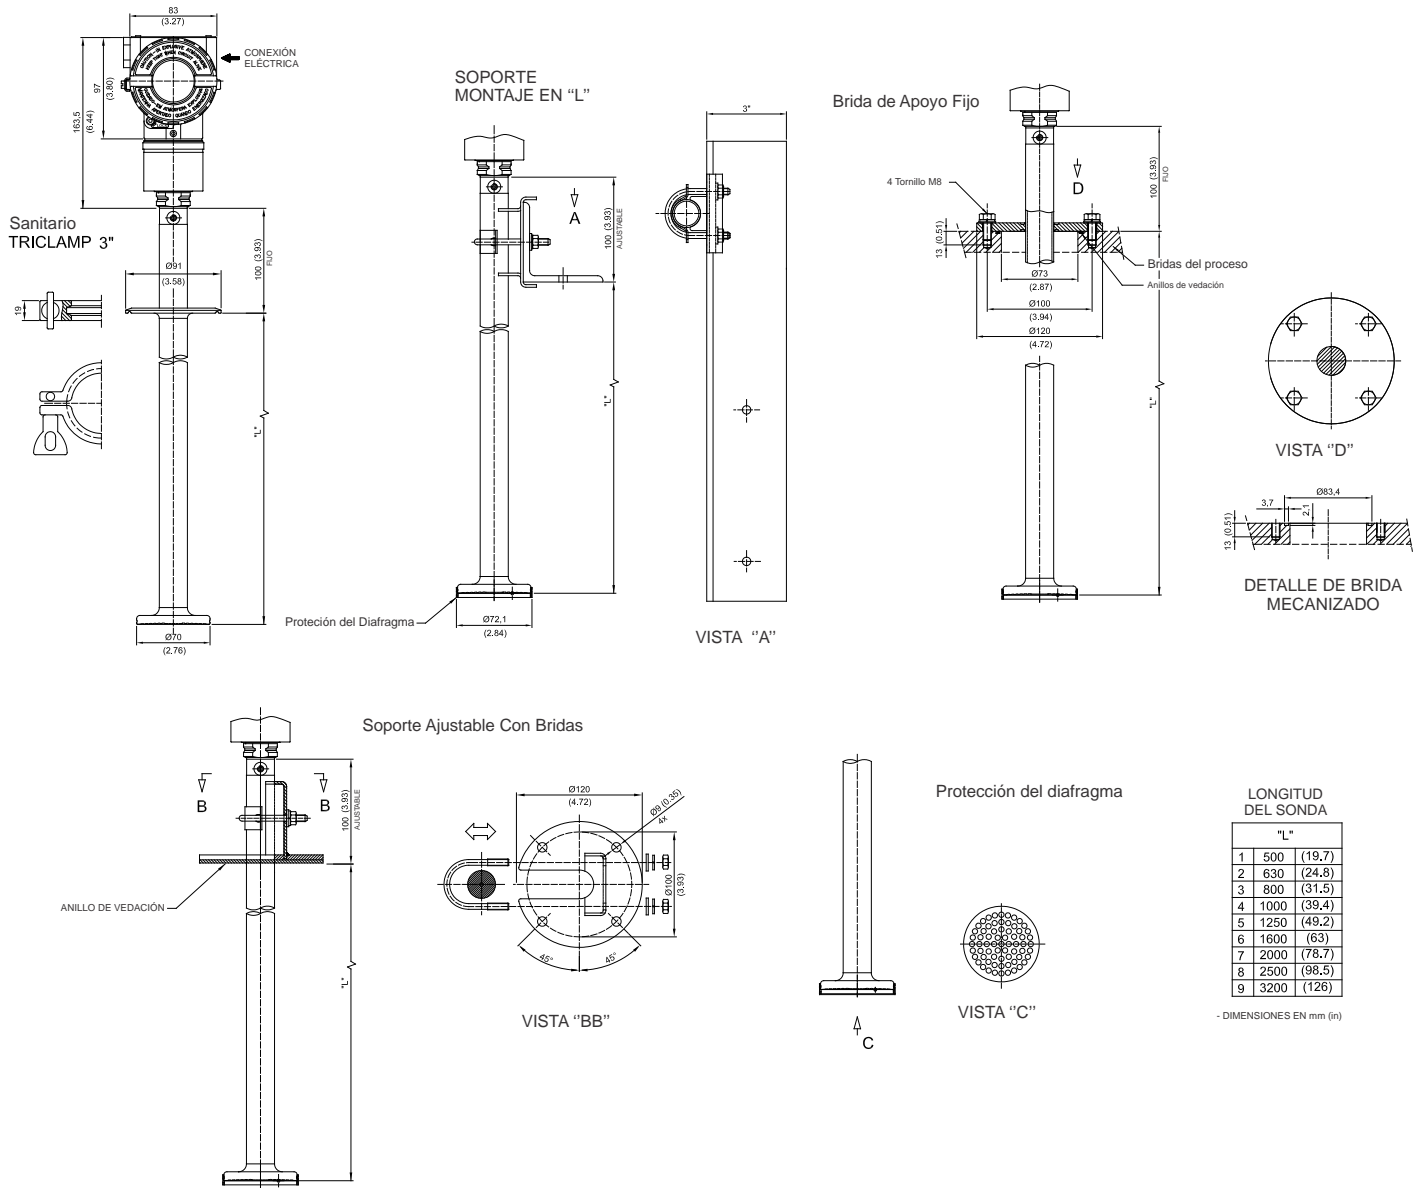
(e) – Diseño Dimensional de Montaje del LD290 - Inserción
